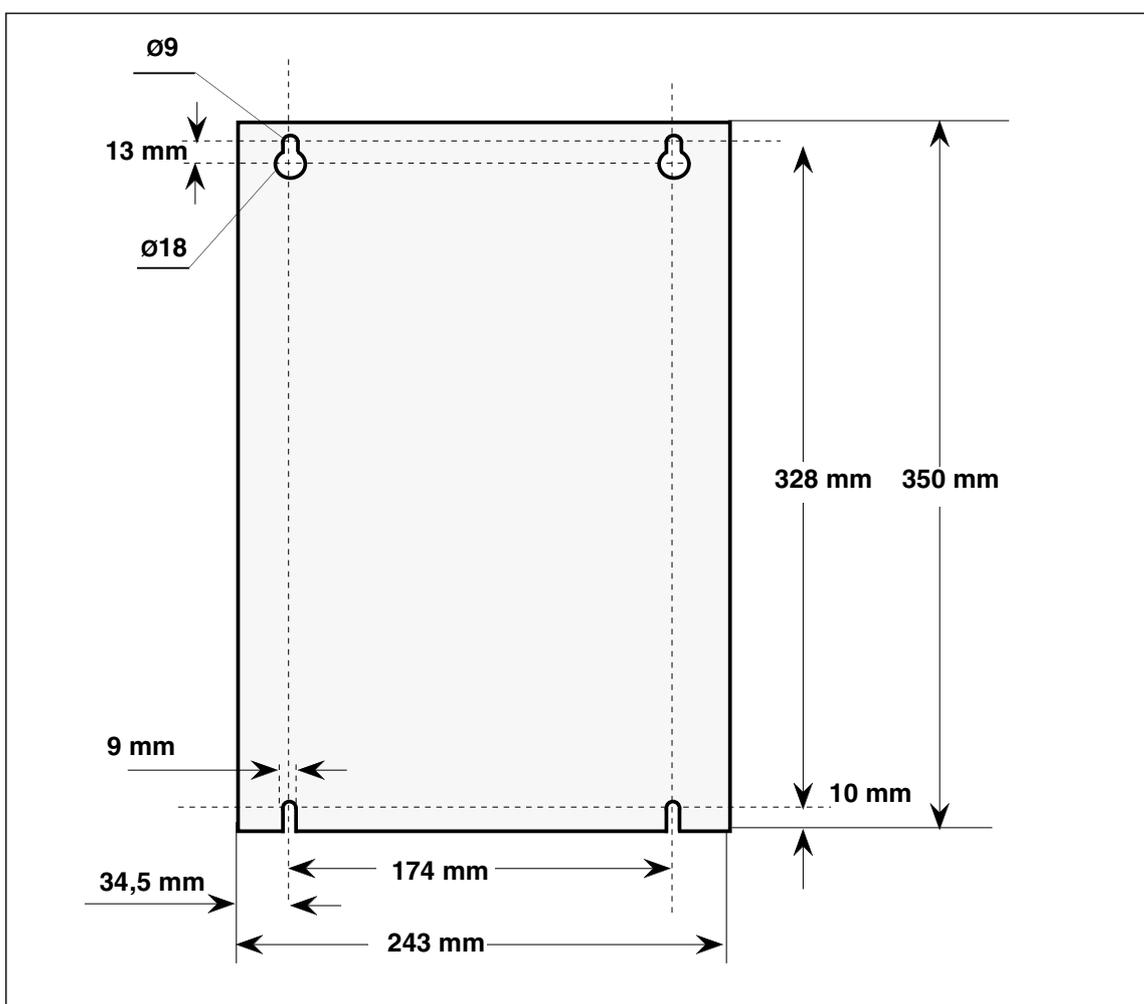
Détails de fixation et les dimensions hors tout (vue de face)
